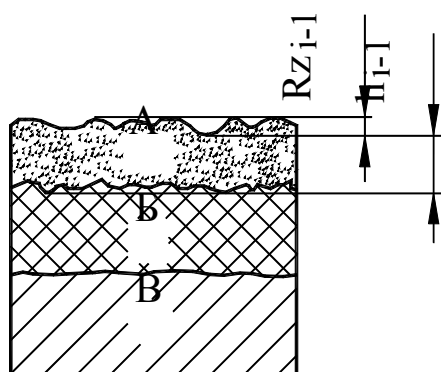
Схема поверхностного слоя после обработки наружной поверхности заготовки [35]
